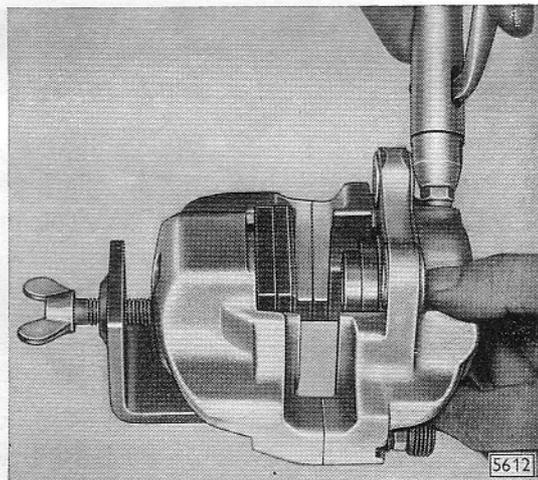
Kolben aus Flanschgehäuse des Bremsattels herauspressen
